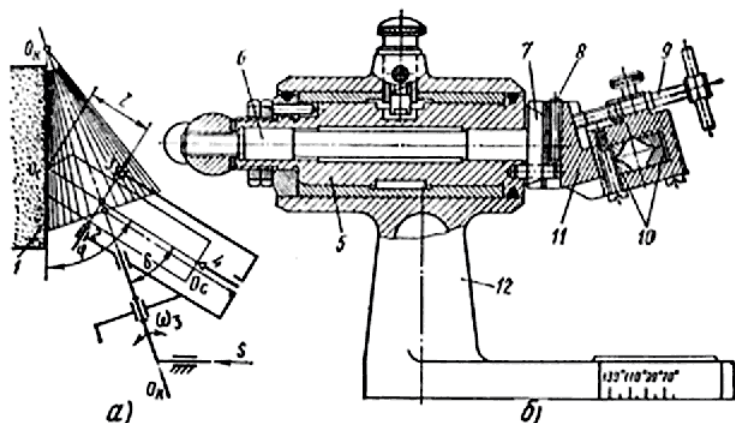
Приспособление для заточки сверла с конической задней поверхностью
